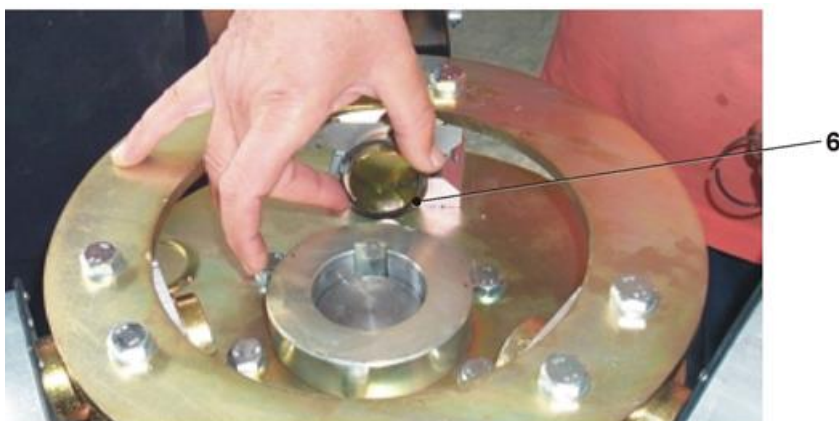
Montage des pale desassemblées, réglage de l'écart.
